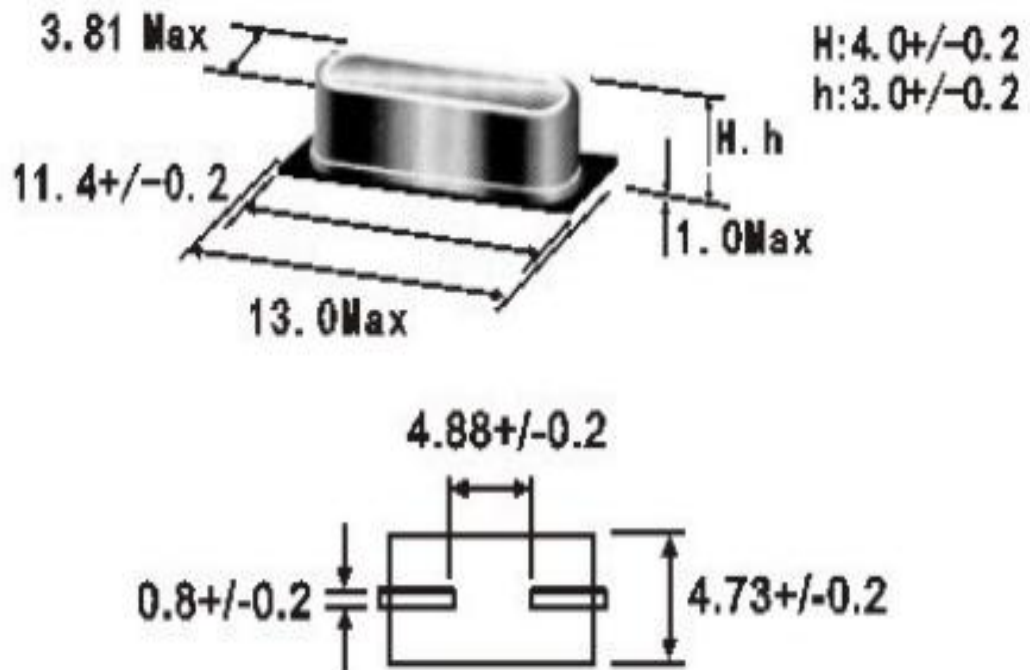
Габаритні розміри кварцового резонатора 4М-49SMD-SR
